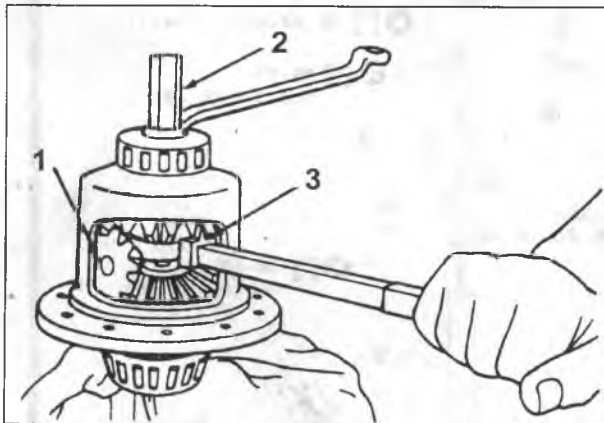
1. Сателлит. 2. Болт сжатия дисков. 3. Приспособление.
